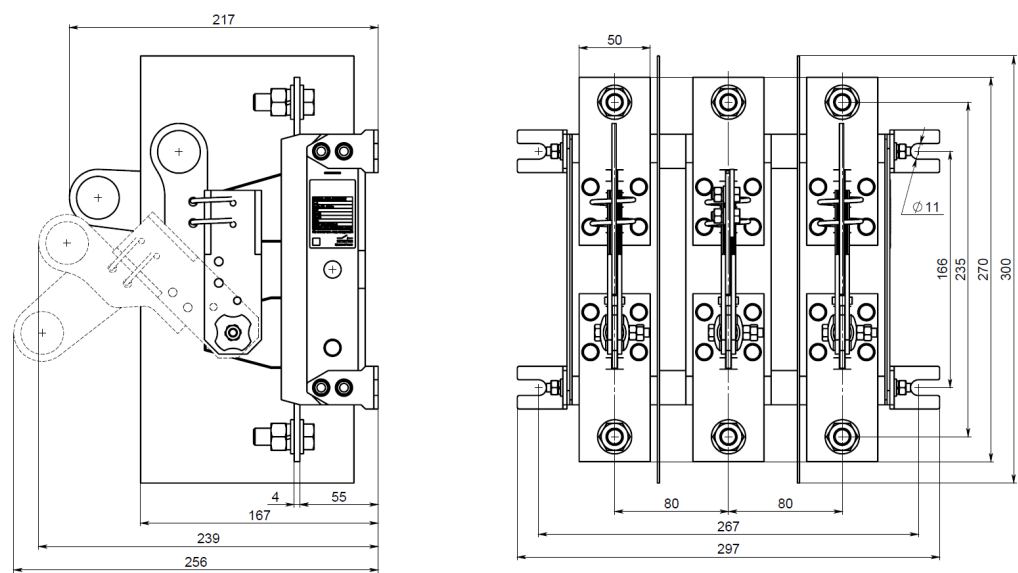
Разъединитель РЕ19-41(43)-31120-00 с боковой рукояткой
